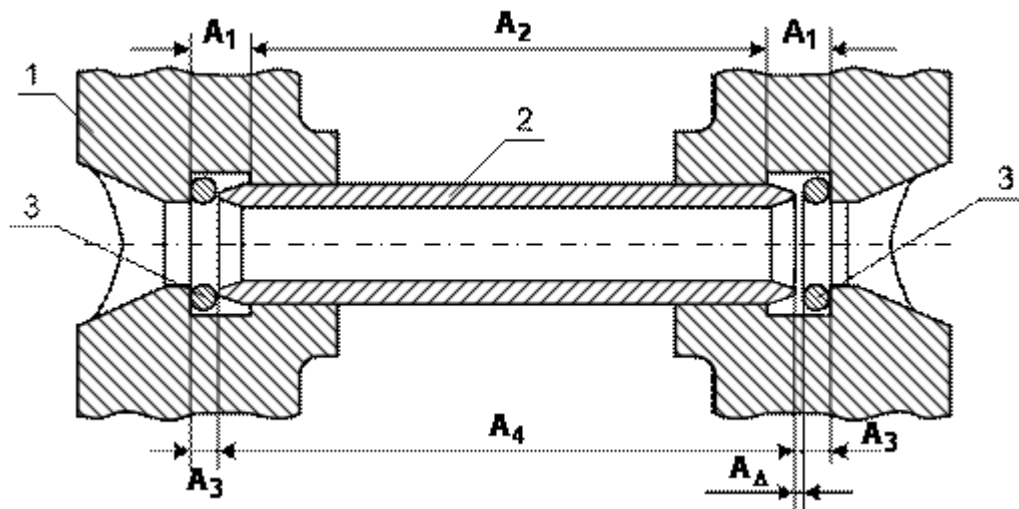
Сборочная единица: 1 – поршень; 2 – палец; 3 – стопорное кольцо
